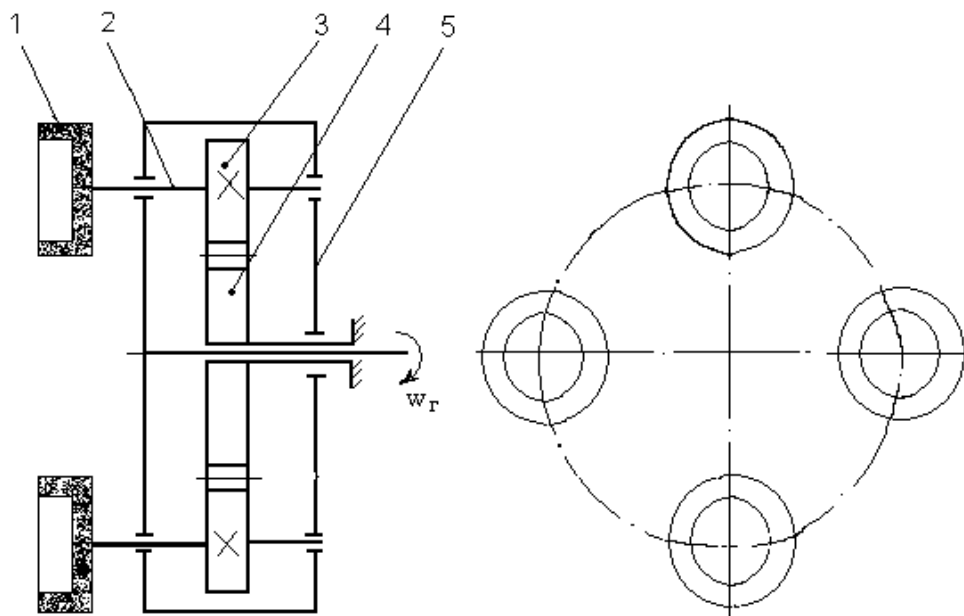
Кинематическая схема планетарной головки: 1 – шлифовальный круг; 2 – шпиндель; 3 – зубчатое колесо (сателлит); 4 – неподвижное зубчатое колесо (в случае наружного зацепления); 5 – корпус головки
